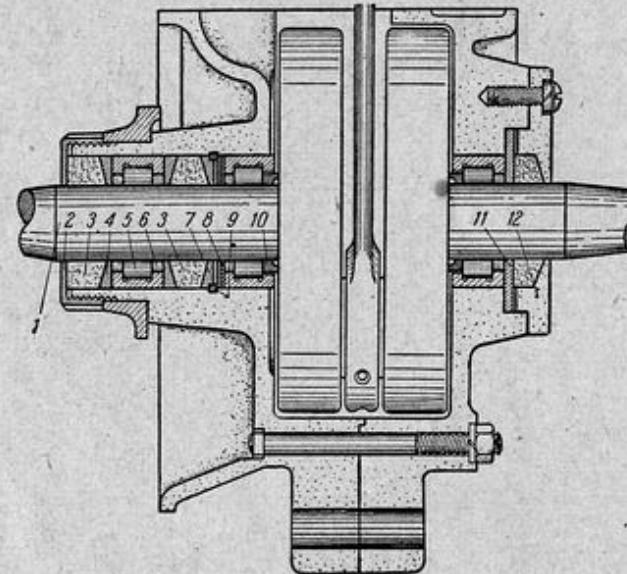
Сальники коренных подшипников двигателя Л-300:
